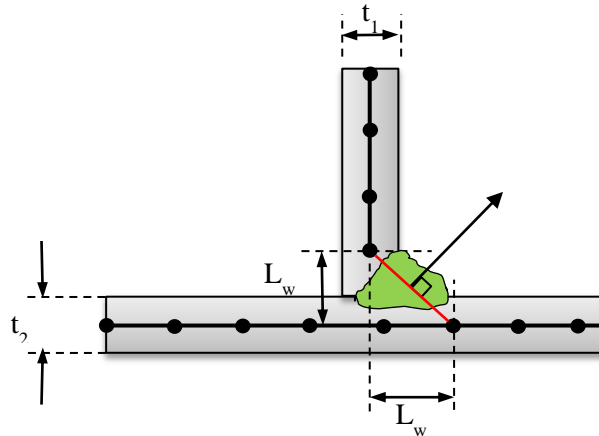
Elementos para soldadura tipo *chaflán
